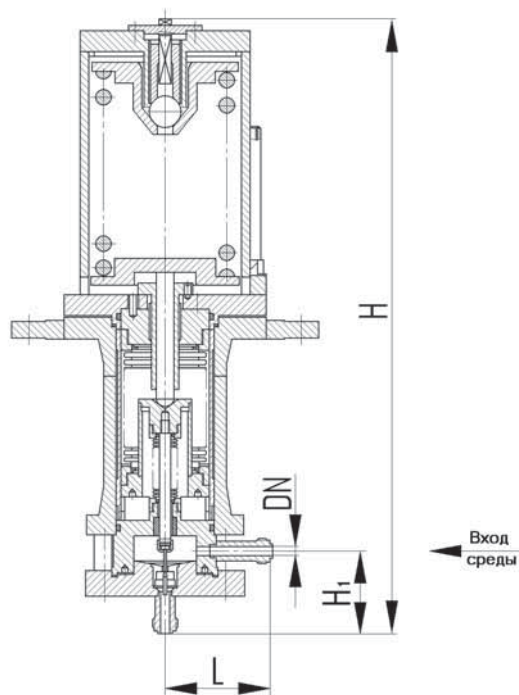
Клапан регулирующий угловой штуцерный
